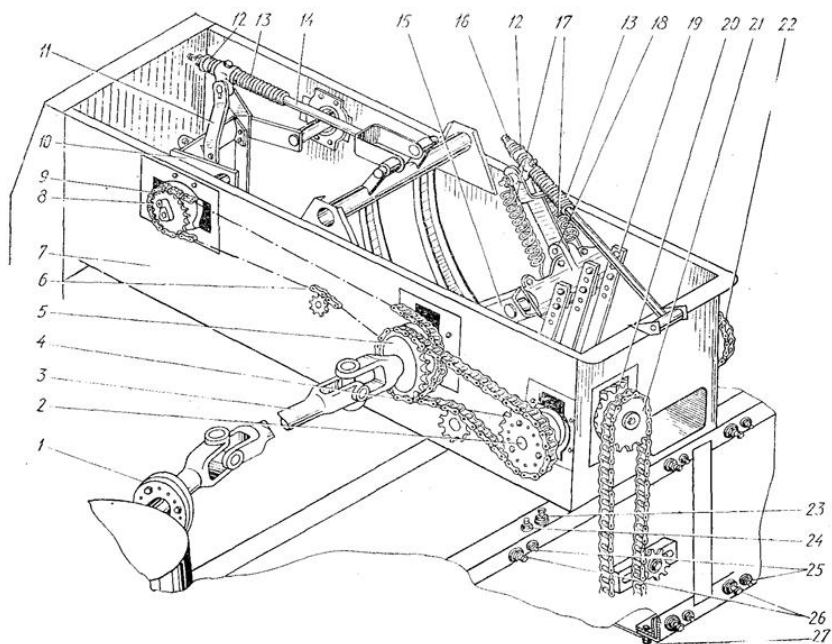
Механизм упаковщиков: 1-фланцевое соединение; 2-ведущий вал; 3-карданная передача; 4-регулируемое соединение вязального аппарата; 5-блок звездочек; 6-цепь; 7-рама; 8-срезная шпилька заднего упаковщика; 9,21,22-звездочки; 10-коленчатый вал заднего упаковщика; 11-зубья заднего упаковщика; 12-амортизатор; 13, 17-пружины; 14-задняя качалка; 15-коленчатый вал переднего упаковщика; 16-передняя качалка; 18- срезная шпилька переднего упаковщика; 19-зубья переднего упаковщика; 20-коническая шестерня; 23, 26-упорные болты; 24, 25, 27-винты
